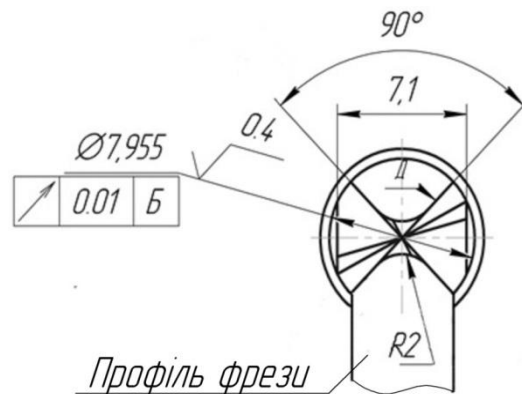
Профіль фрези для прямої канавки реверсивного свердла
